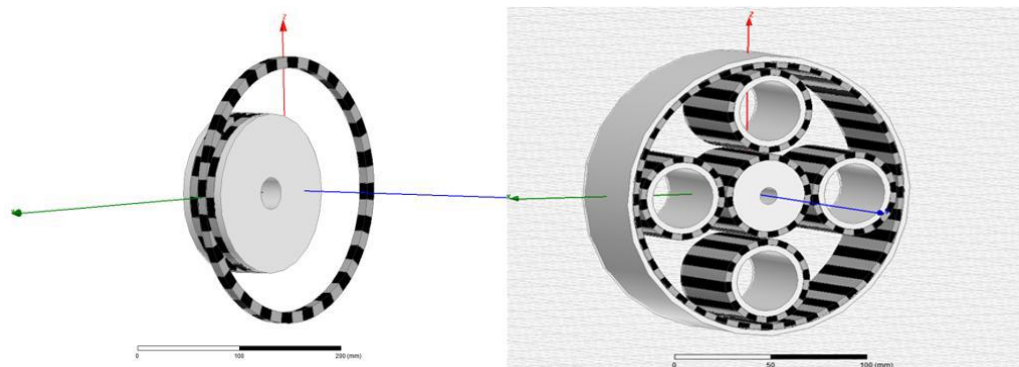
(1) Магнитный цилиндрический зубчатый венец 1: 2, максимальный крутящий момент: 24,2 Нм. (Справа) 1: 5 Магнитная цилиндрическая зубчатая передача, максимальный крутящий момент: 32 Нм.
